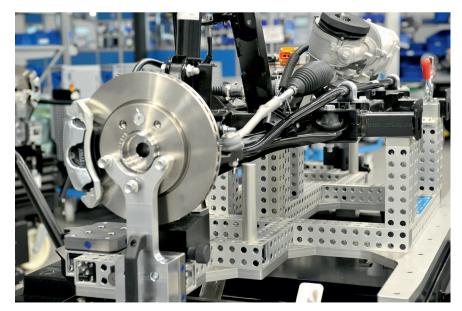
Ursächlich ausgelegt für reproduzierbare Werkstückaufnahmen in der dimensionellen Messtechnik sowie Fertigungstechnik, eignet sich das Spann- und Fixiersystem auch für hochpräzise Montagevorrichtungen, hier etwa zur Achsmontage. © Witte
